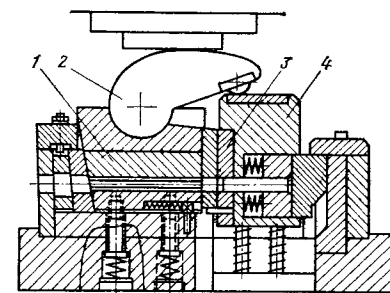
Конструктивная схема штампа для закрытой отрезки коротких заготовок от алюминиевых прутков
